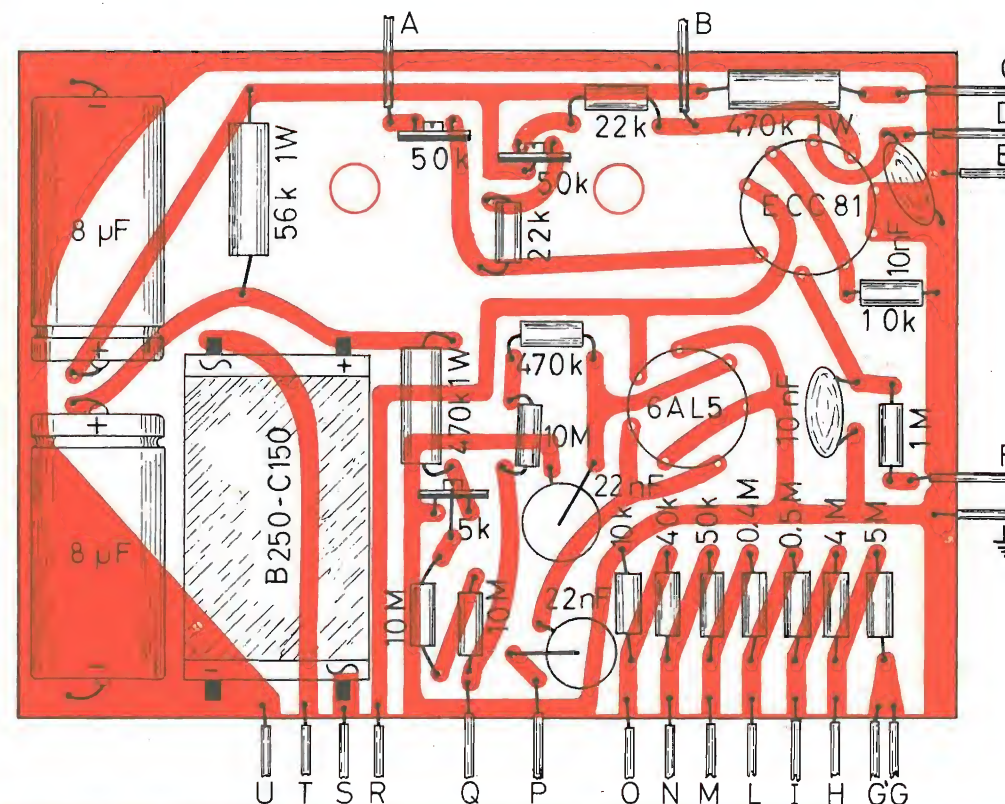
Circuito stampato visto dal lato dei componenti.
